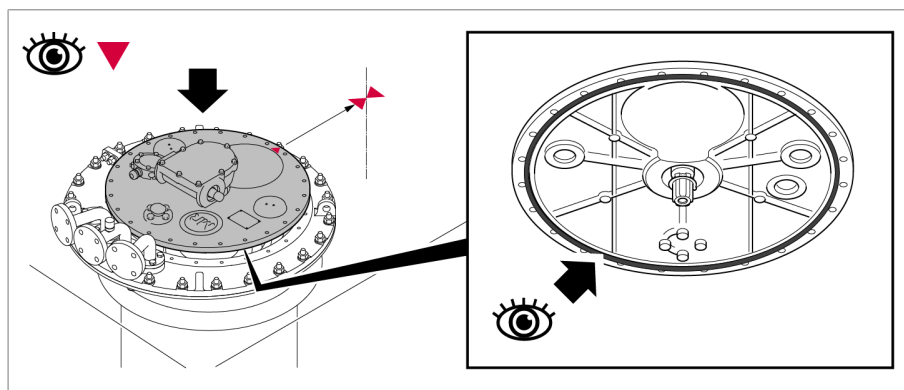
Laststufenschalterkopfdeckel mit O-Ring
